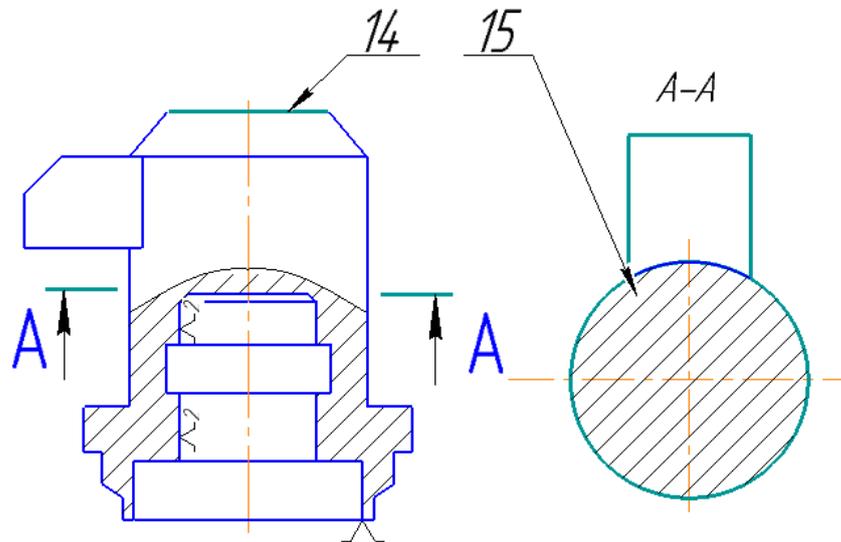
Эскиз фрезерной операции с ЧПУ 015, установ А
